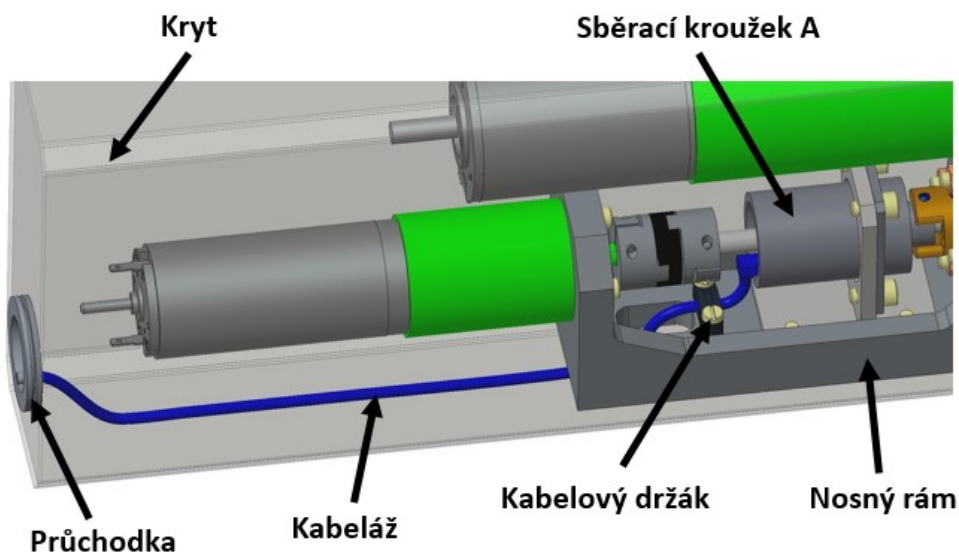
Vedení kabeláže od tenzometrického převodníku
